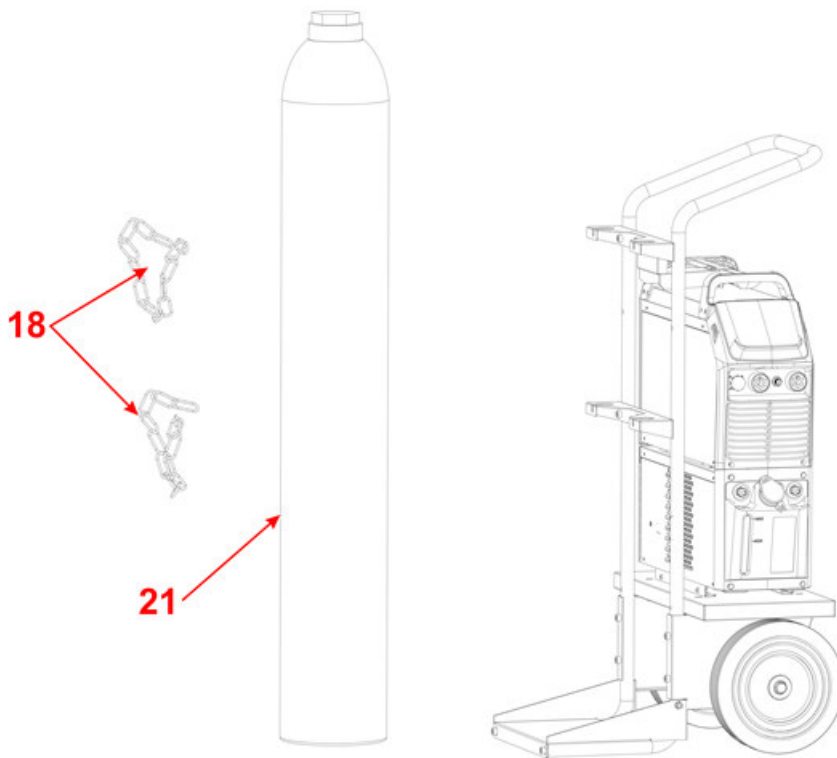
Montage des Schweißgerätwagens Schritt 7
